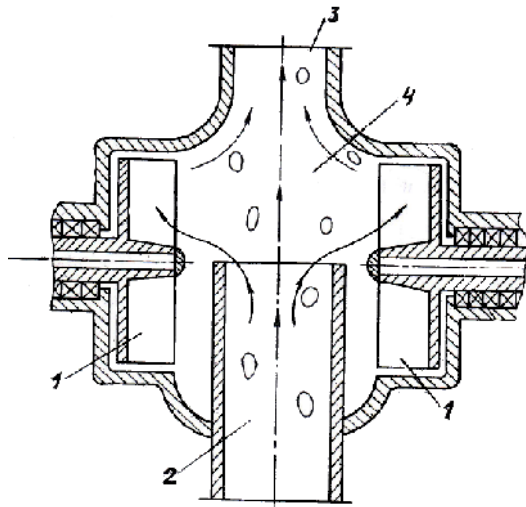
Двухвальный свободновихревой насос с соосным расположением валов: 1 – рабочее колесо; 2 – подвод; 3 – отвод; 4 – свободная камера
